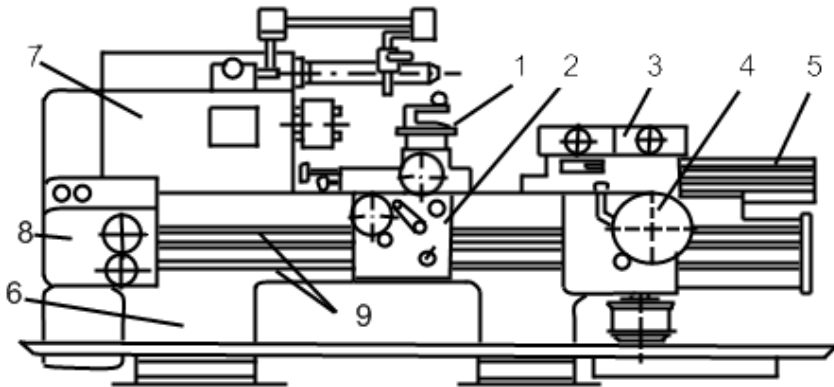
Загальний вигляд токарно-револьверного верстату
